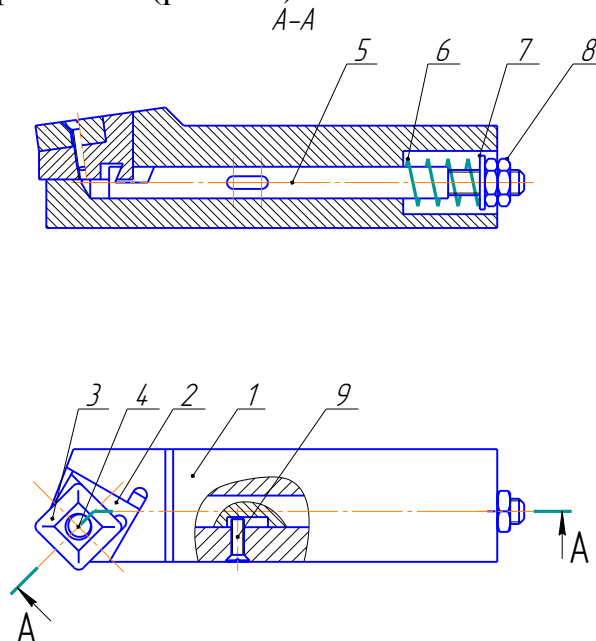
Різець з прискореною зміною робочої частини
